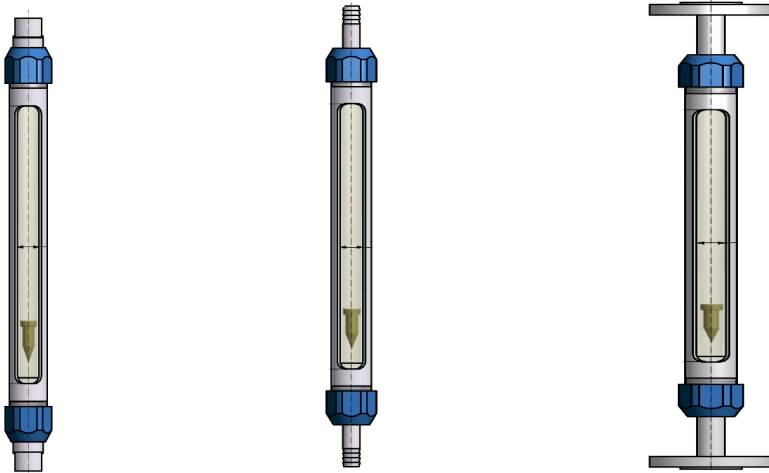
TUBUX M30 mit Innengewinde, Schlauchtülle und Flanschanschluss
